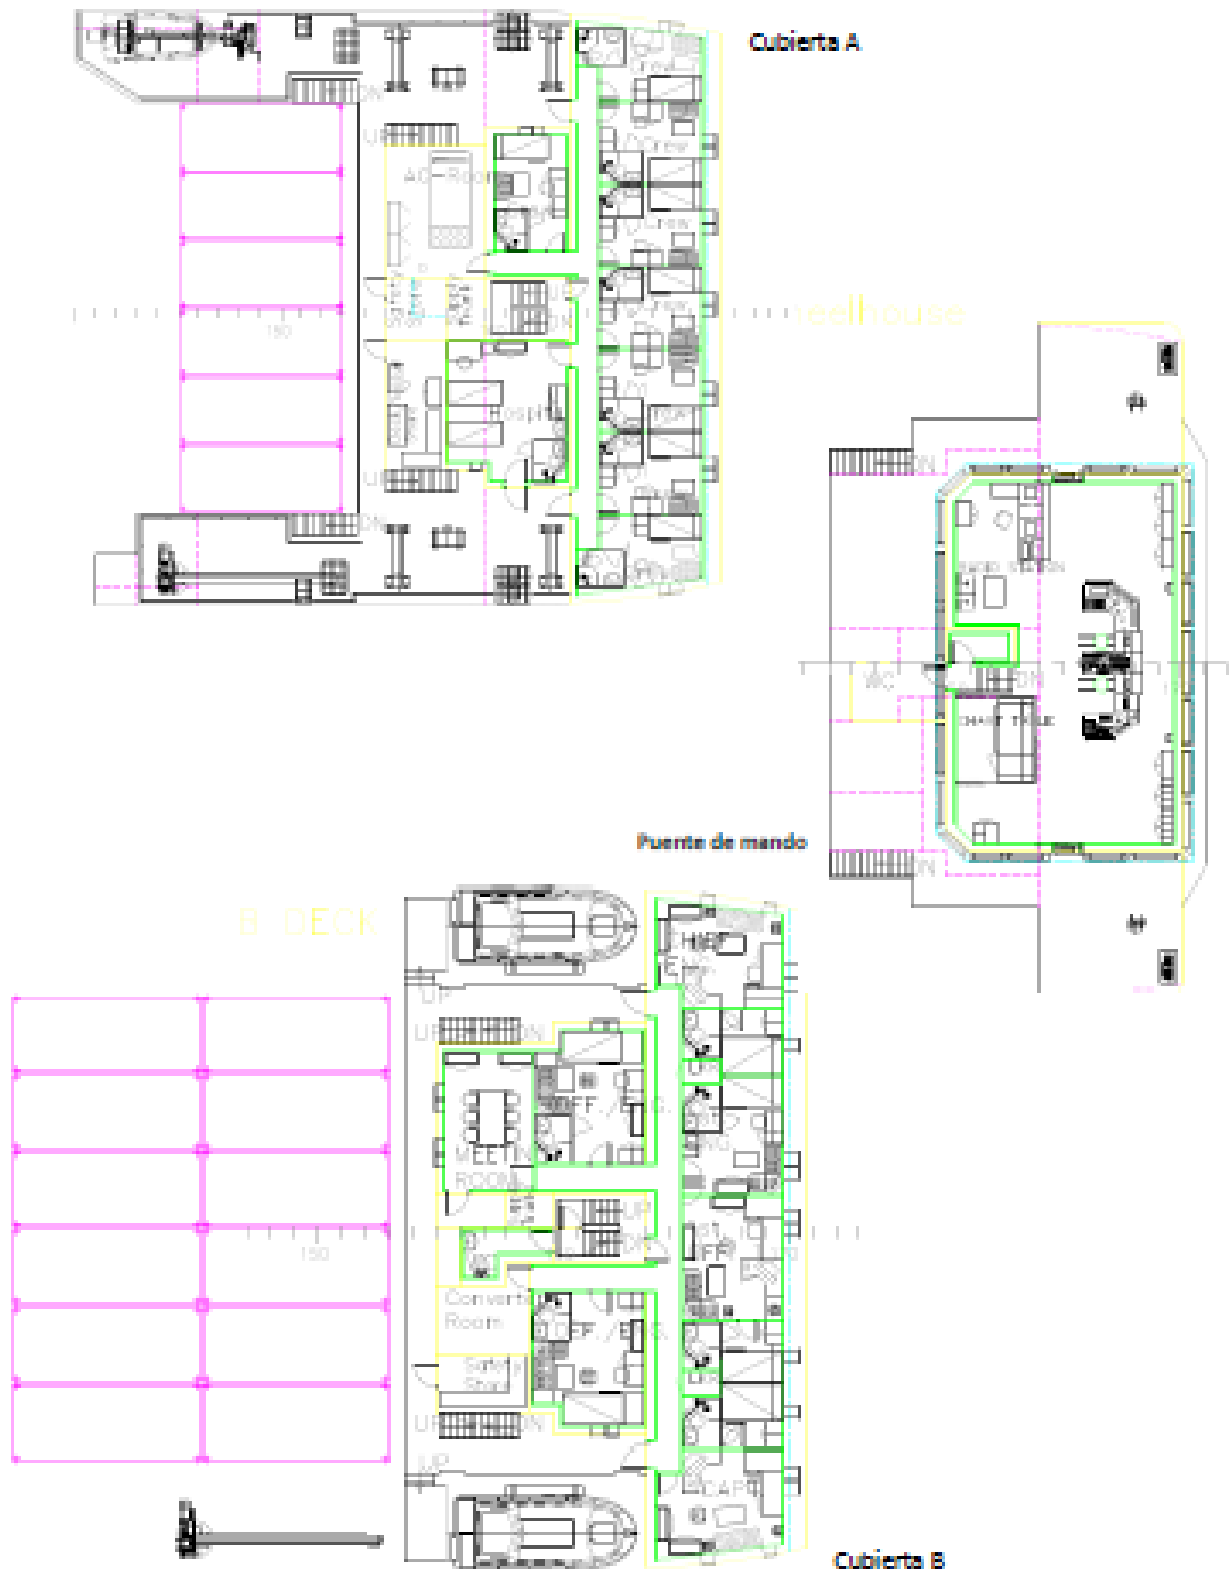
cubierta A, puente de mando y cubierta B
